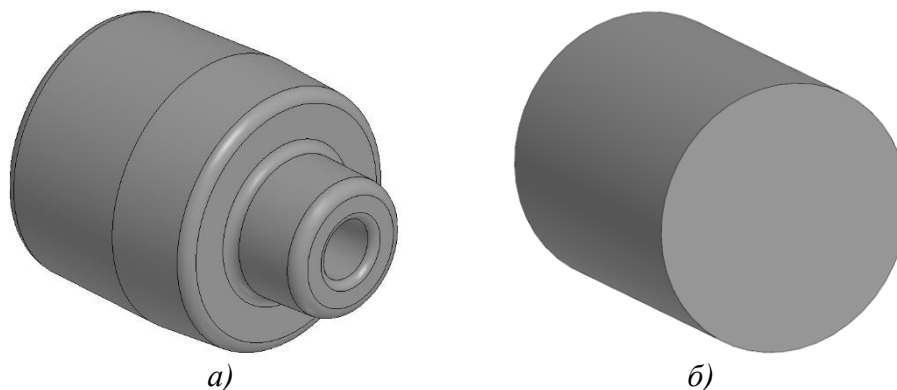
Заготовки детали «Корпус коллектора»: а – получена литьём под давлением, б – получена из проката.
